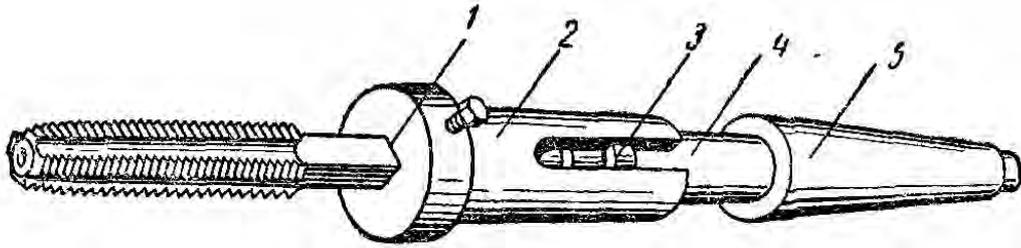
Приспособление для закрепления метчика при нарезании резьбы на токарном станке
